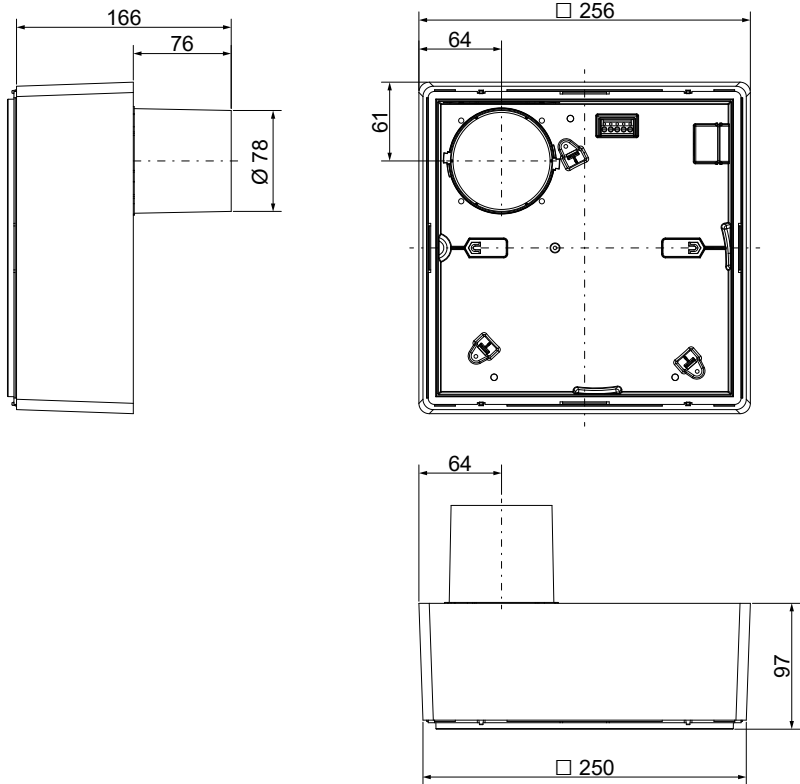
Maßzeichnung – Gehäuse Abluftventilator Taris AP
